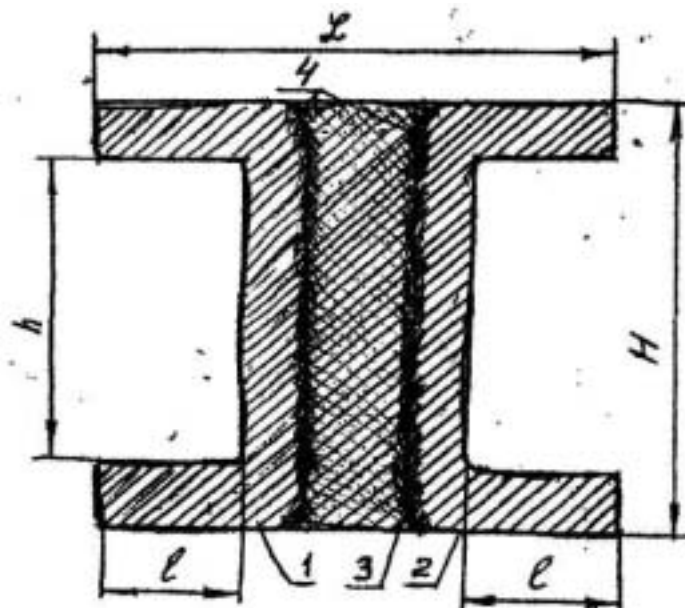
Схема расчетного элемента стенки ВПСТ труб из ПНД (А из рис. 1)
